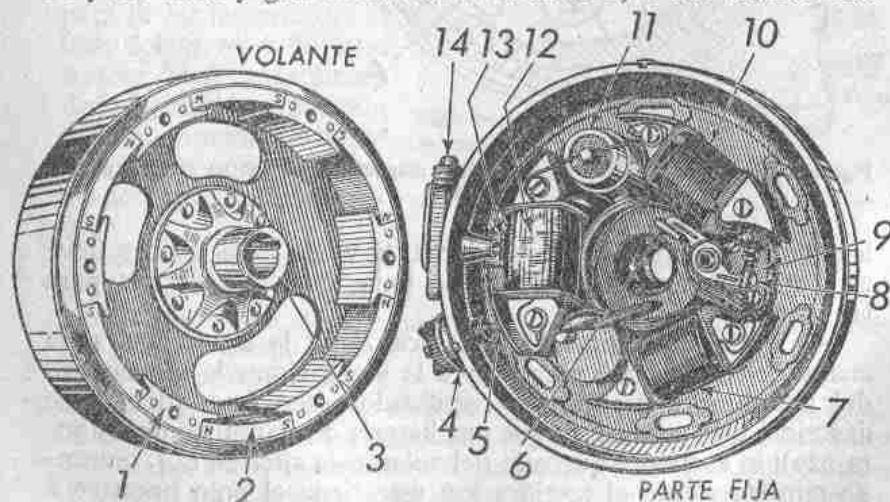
Volante magnético con dos bobinas para alumbrado.
